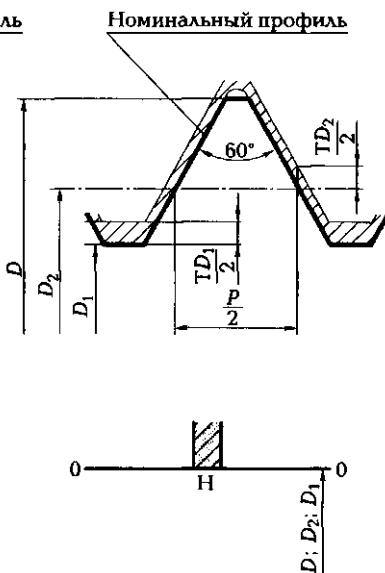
Схемы расположения полей допусков посадок с зазором
